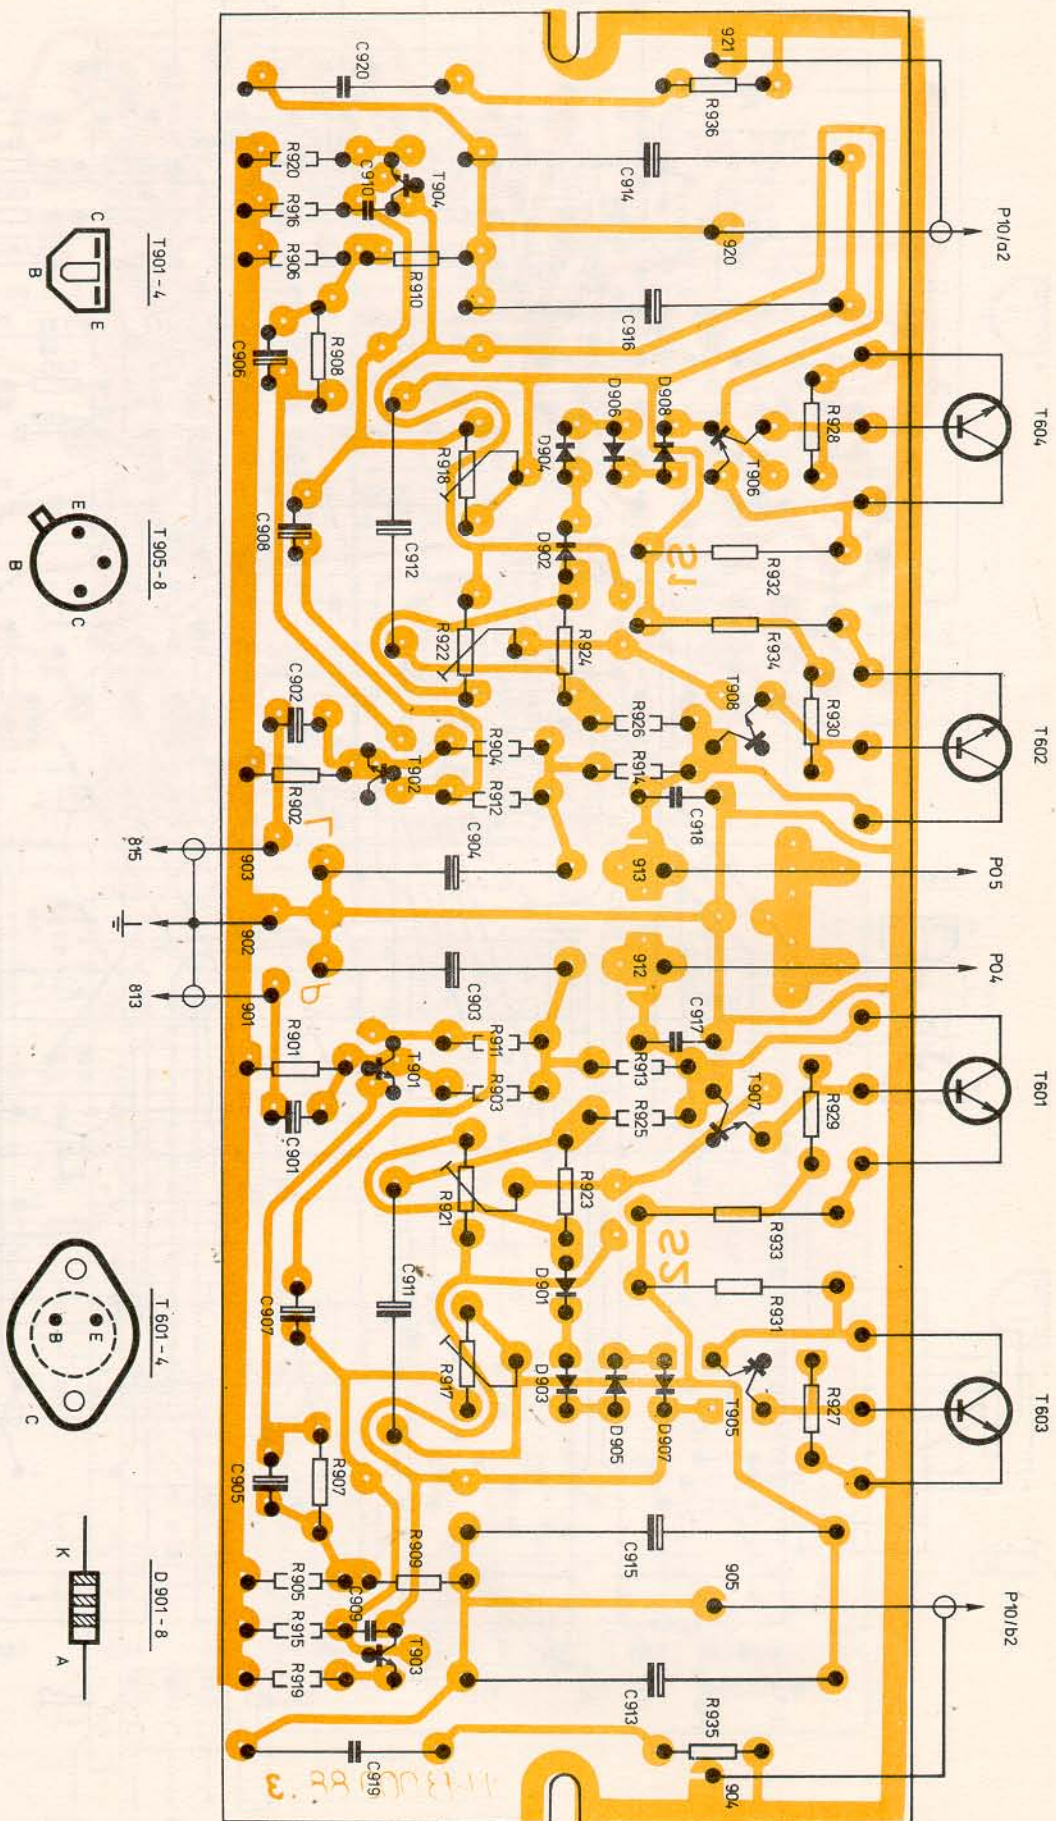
Montážní zapojení korekčního předzesilovače pro přenosku
